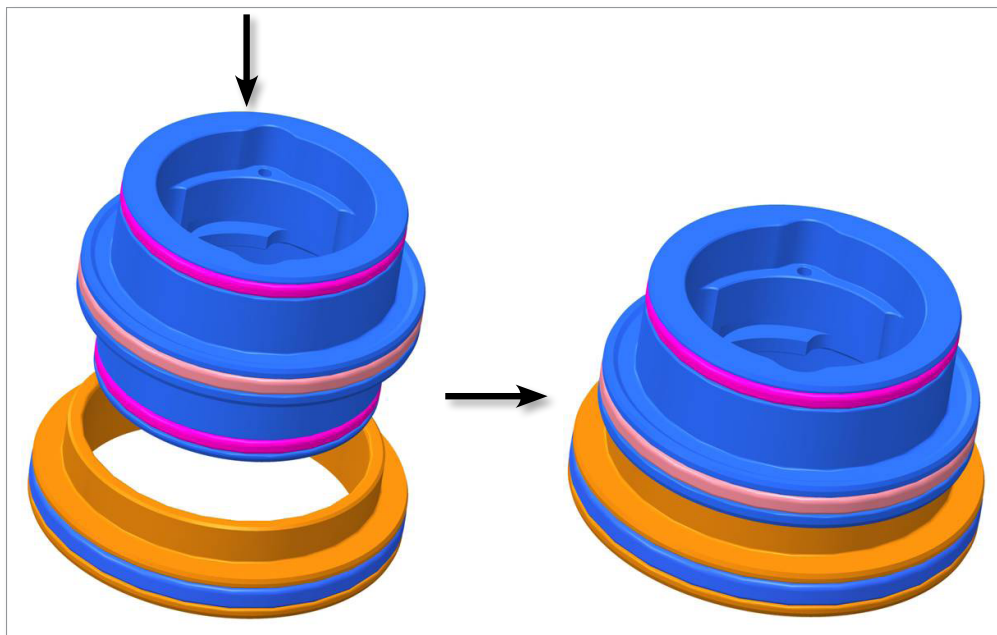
Installazione della parte superiore del pistone sulla parte inferiore del pistone
